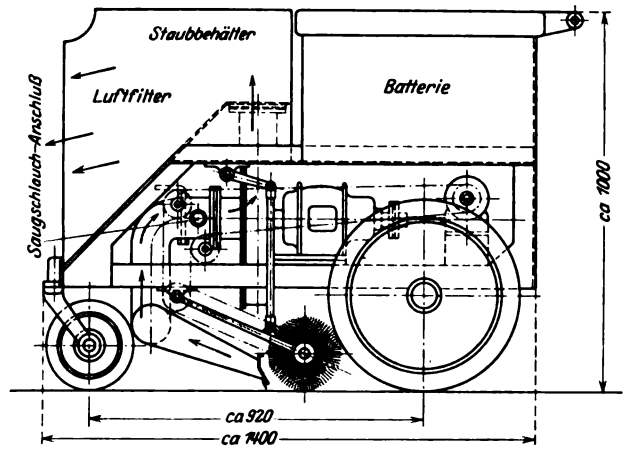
Elektrisch betriebene Vakuum-Kehrmaschine.
